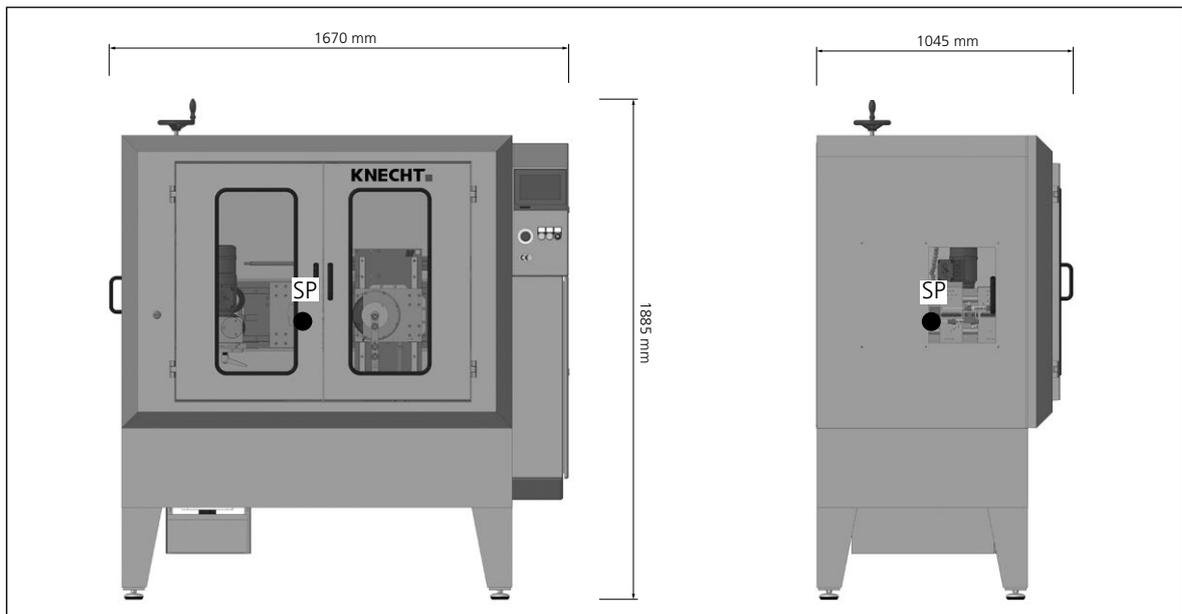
Dimensiones en mm y centro de gravedad (SP) de la máquina
